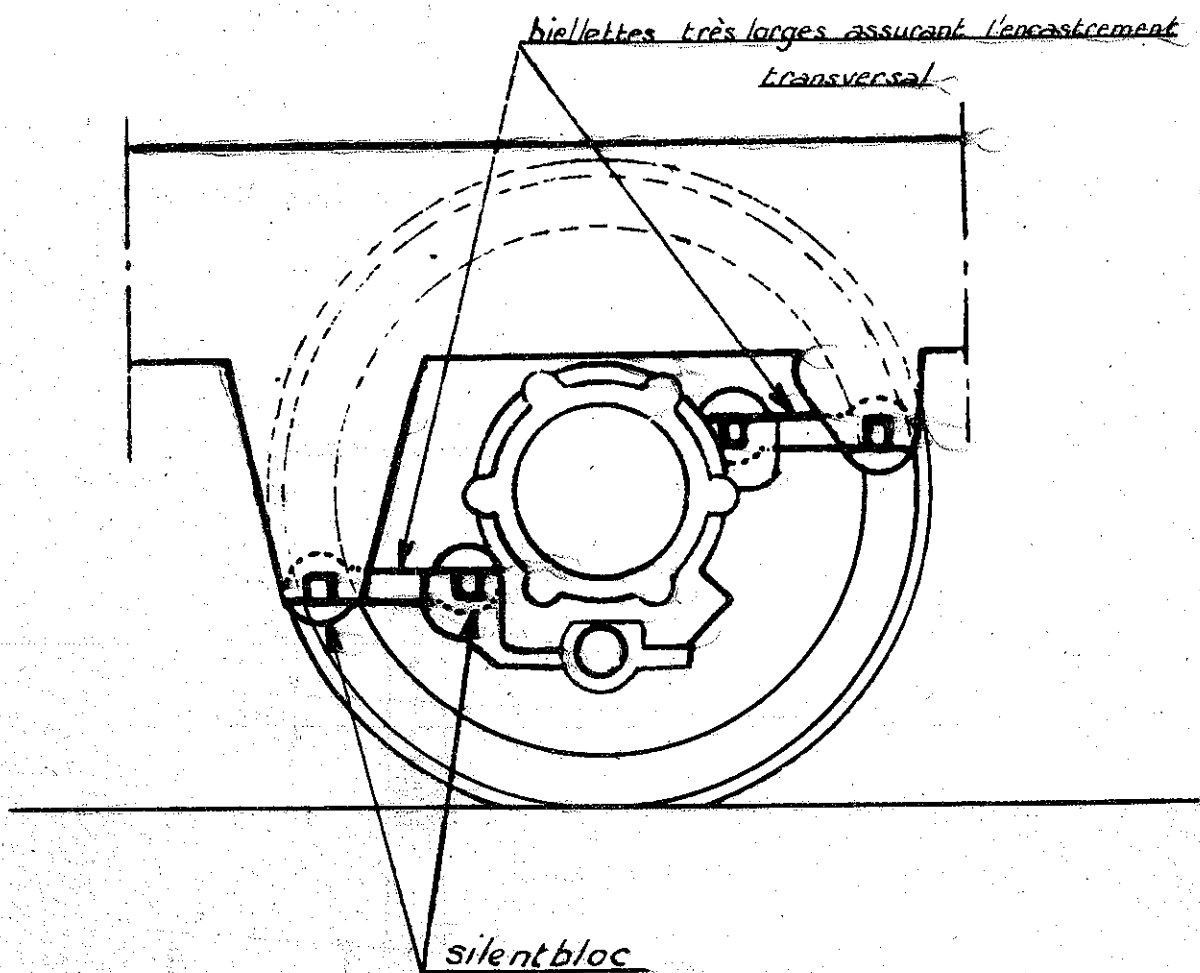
Montage "Alsthom" des boîtes athermos de la 060 DB
